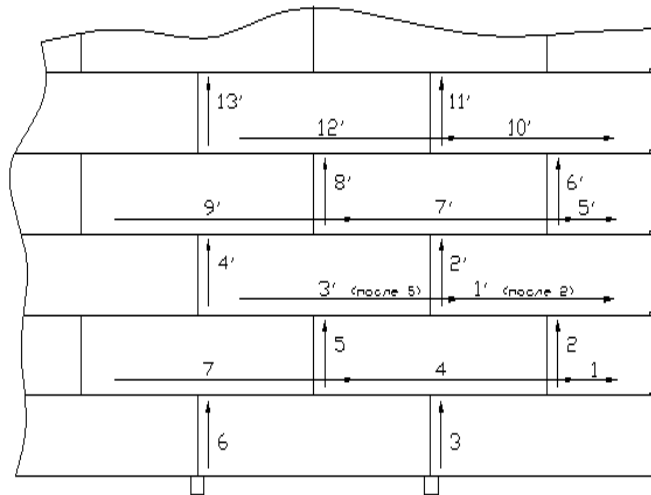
Порядок выполнения сварных швов
